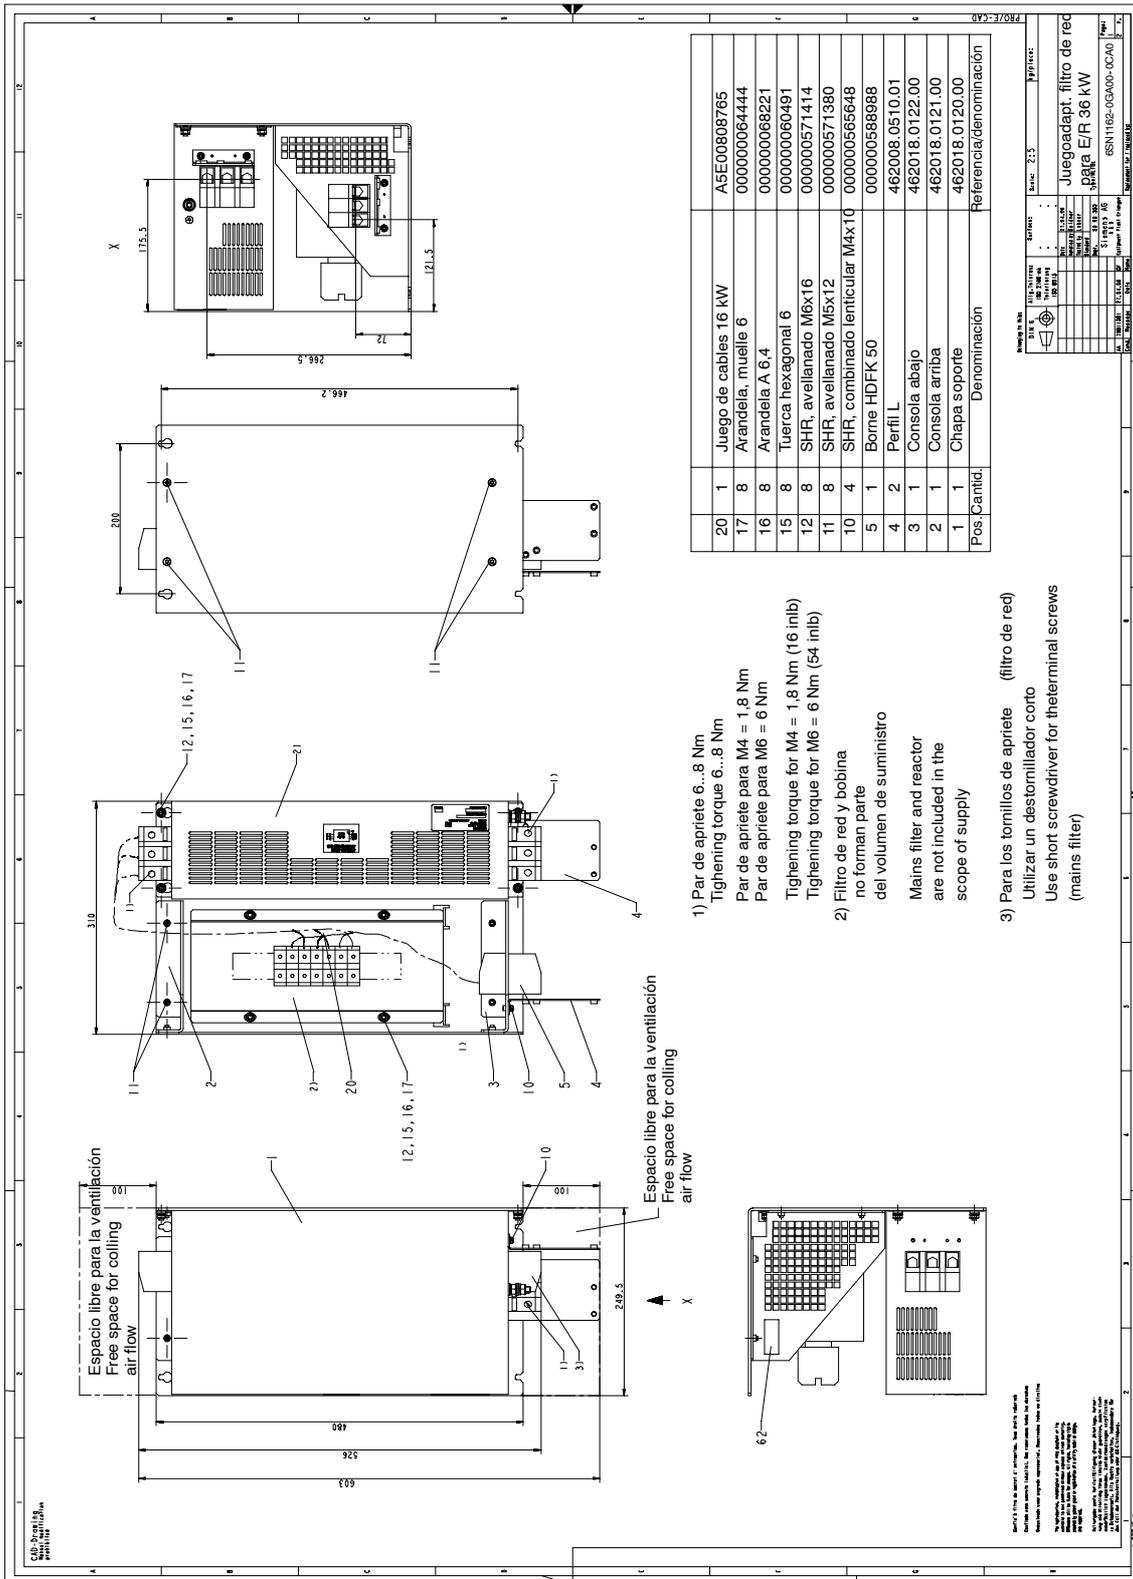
Juego de adaptador filtro de red para módulo E/R 36 kW, 6SN1162-0GA00-0CAx; plano acotado
